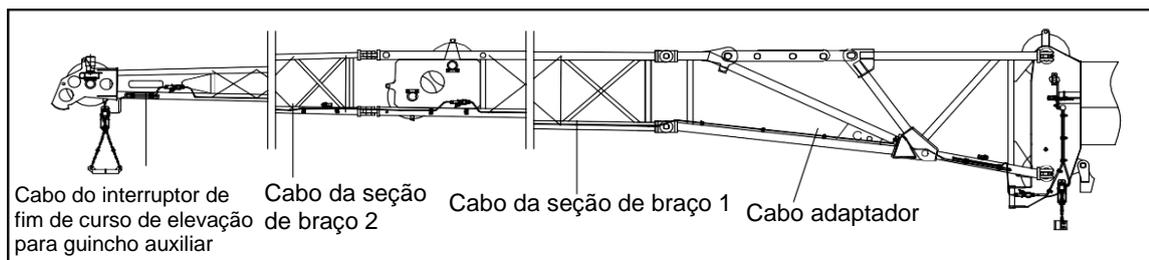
Conexão de cabo com seção de braço 1 e seção de braço 2
